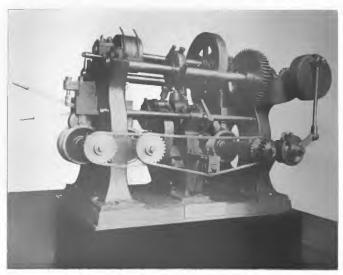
Patent-Winkeleisen-Abgratmaschine.
